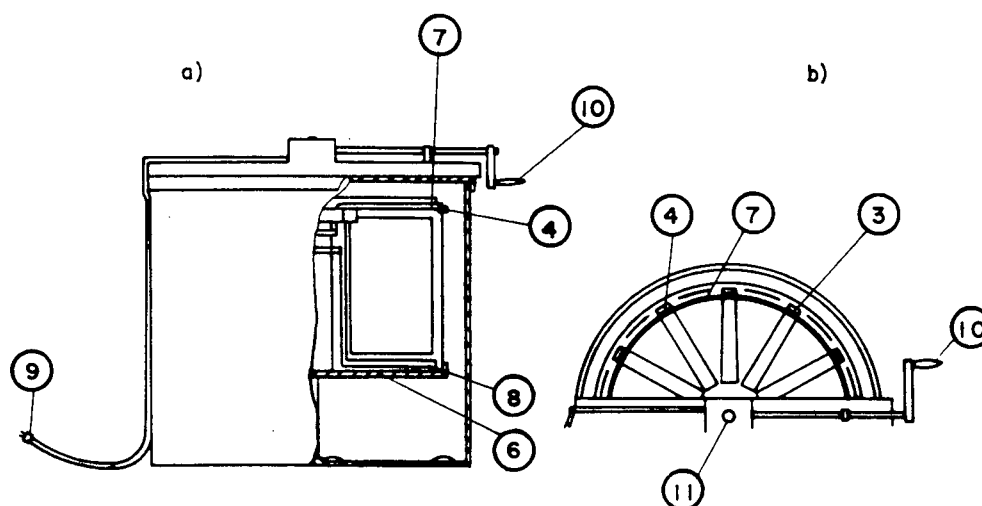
Desenho esquemático da máquina desoperculadora e extratora [17]:
